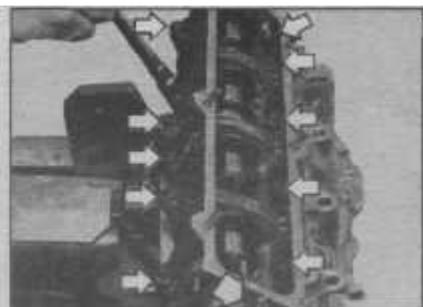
Болты крепления кожуха распредвала (показаны стрелками) (Глава 19)
